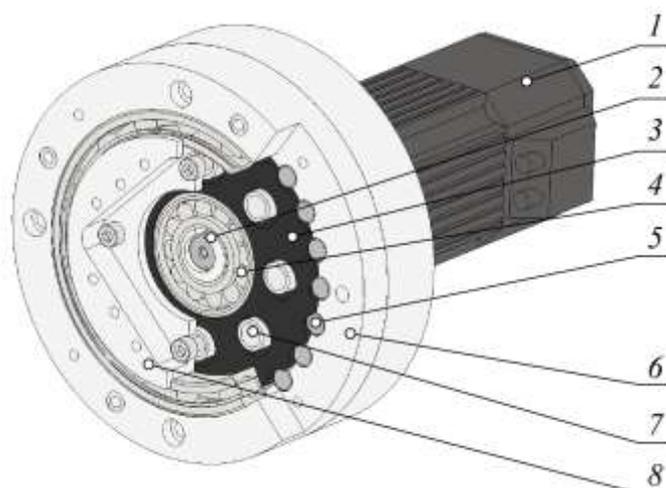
Устройство планетарно-цевочного редуктора по схеме КНВ
